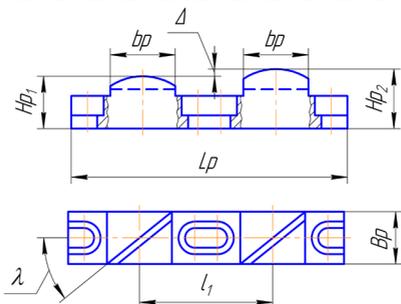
Конструкция резца-зуба развёртки со двоянными безвершинными зубьями с разными диаметрами
